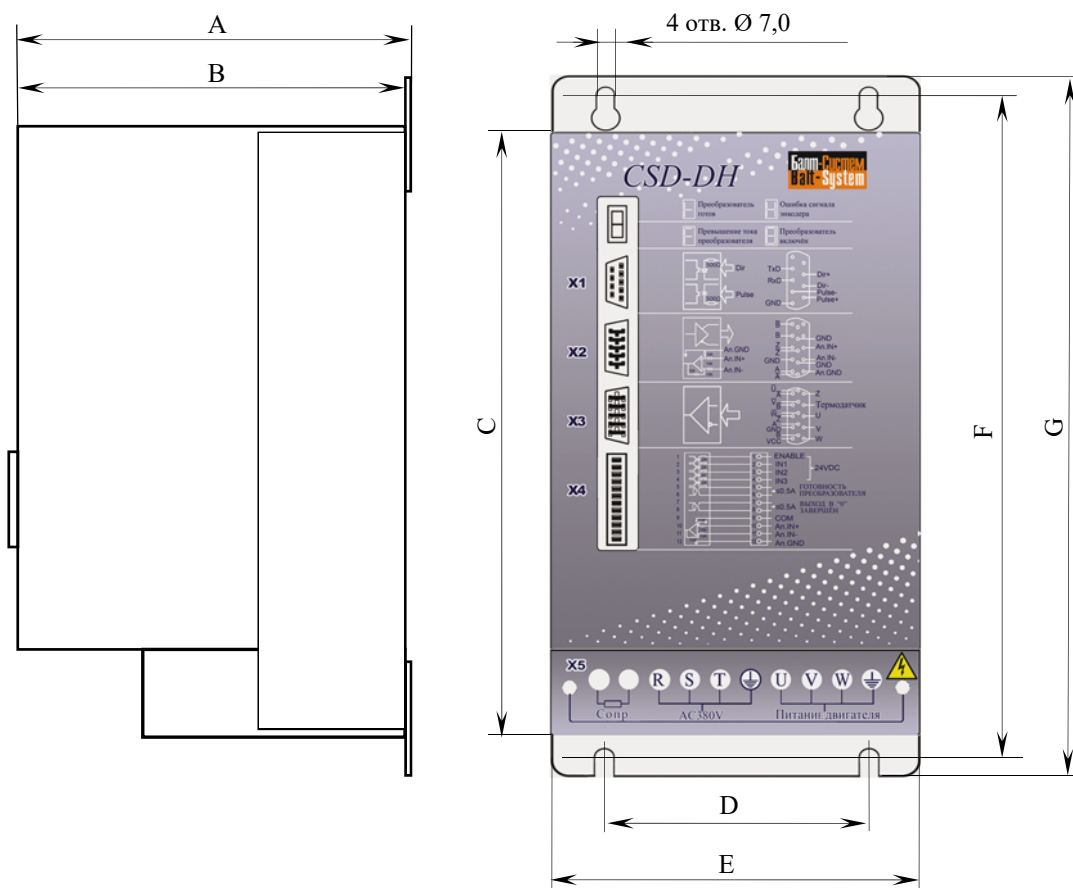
Габаритные и установочные размеры преобразователя
